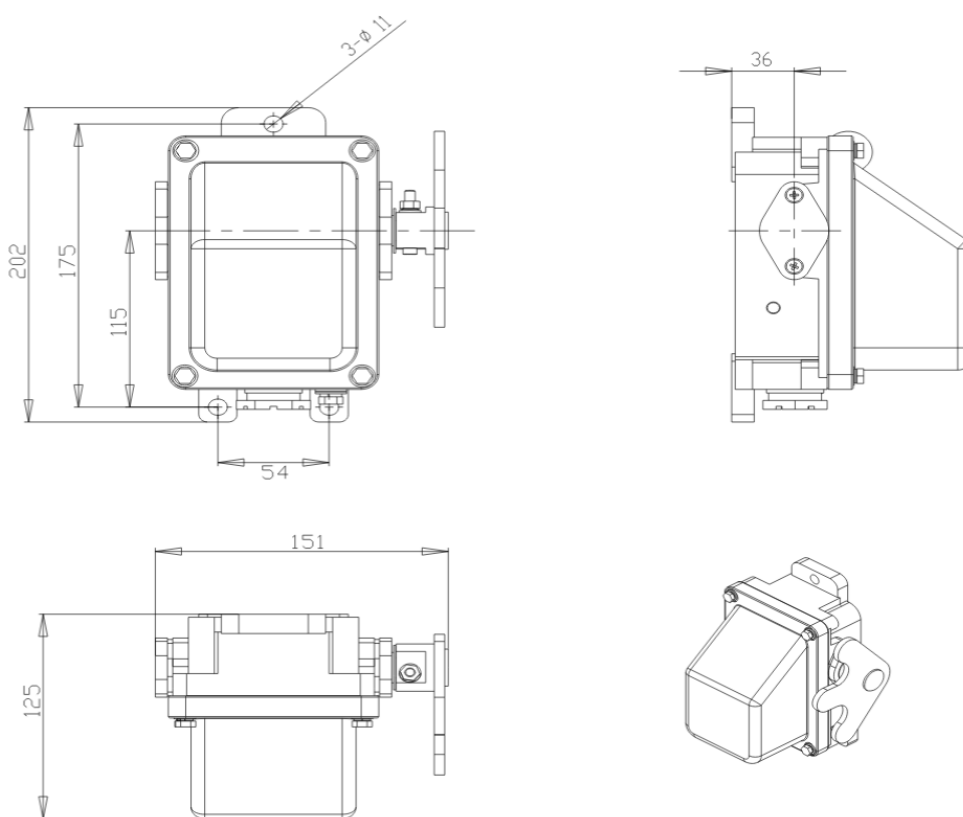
Габаритные размеры концевого выключателя КУ-704
